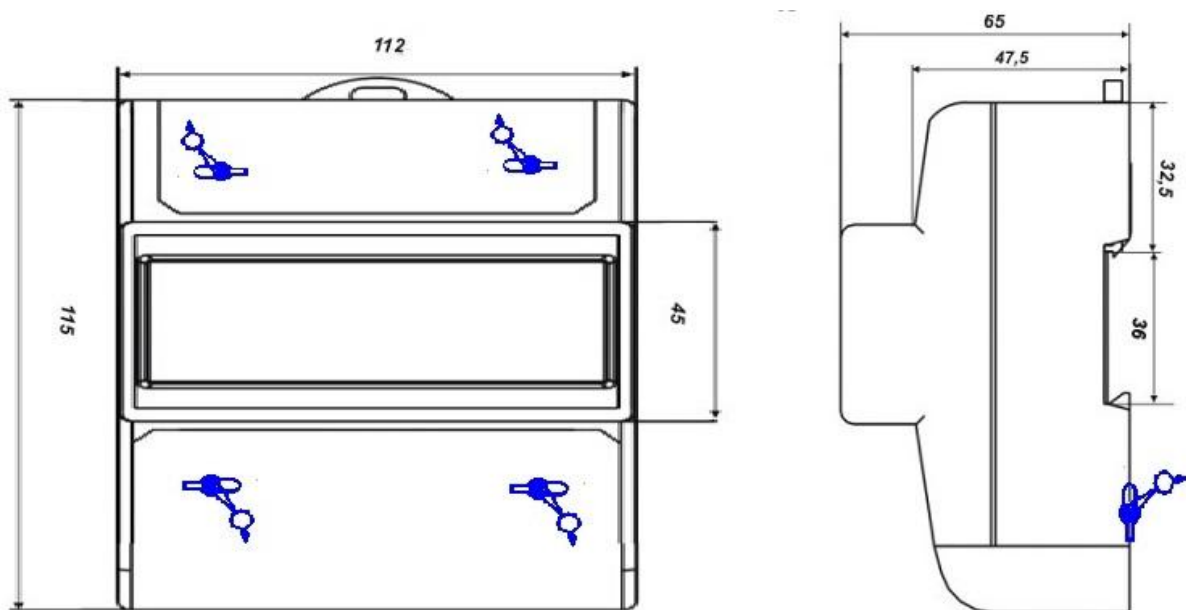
Габаритные и установочные размеры счетчика Н10
